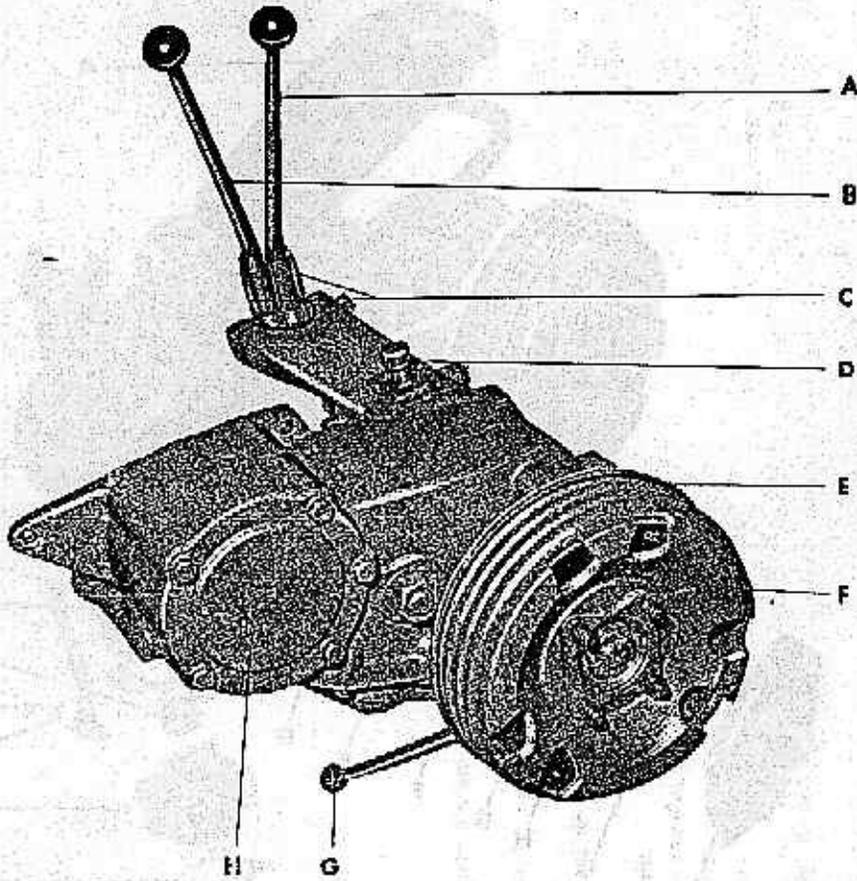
Boîte auxiliaire. Vue d'ensemble.
